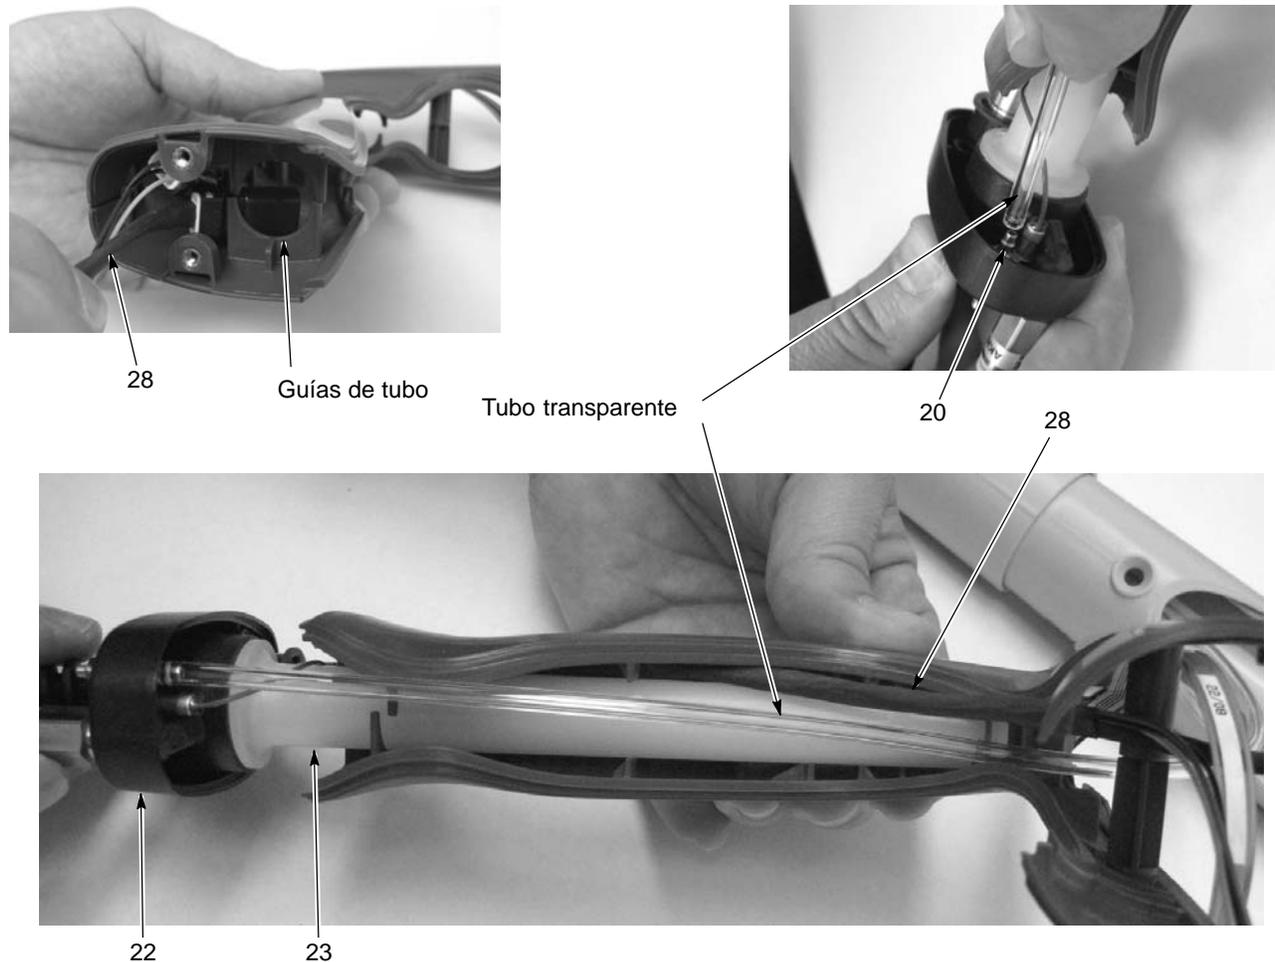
Montaje de las partes de la empuñadura y la base
